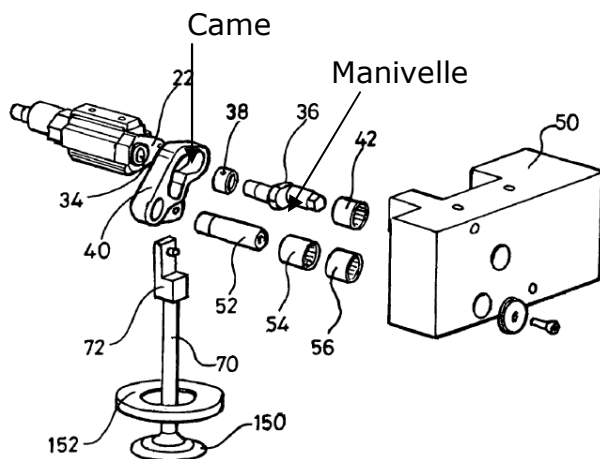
Vue éclatée de la liaison entre le rotor et la soupape [21]
